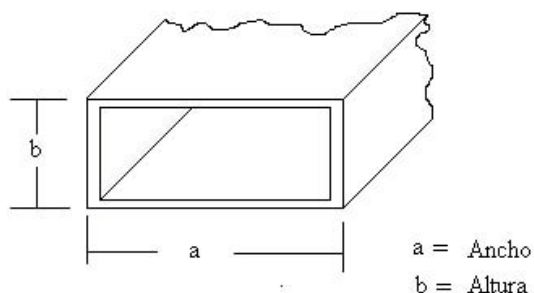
Dibujo que ilustra las dimensiones de una guía de onda; dimensiones internas.
